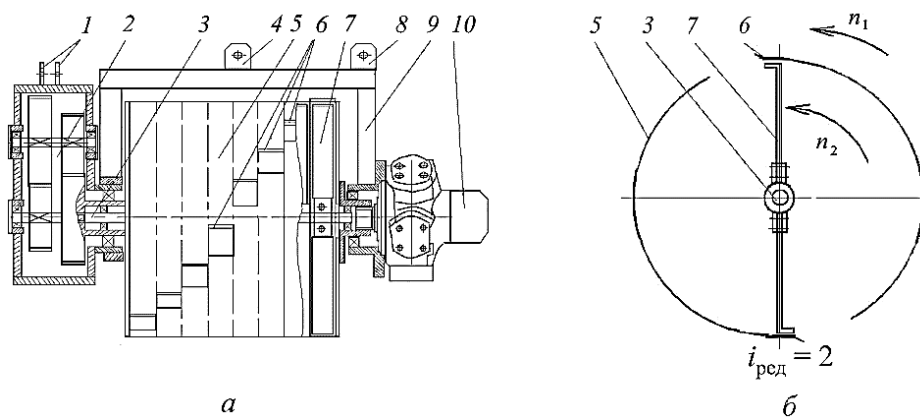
Схемы грунтотема (а) и механизма (б) управления дальностью метания: 1 – кронштейн крепления гидроцилиндра поворота редуктора; 2 – редуктор привода метателей и управления дальностью струи грунта; 3 – вал метателей; 4 – кронштейн навески; 5 – ротор фрезы (вращающийся кожух); 6 – нож; 7 – лопасть метателя; 8 – кронштейн гидроцилиндра управления поворотом в горизонтальной плоскости; 9 – рама; 10 – высокомоментный радиально-поршневой гидравлический двигатель
